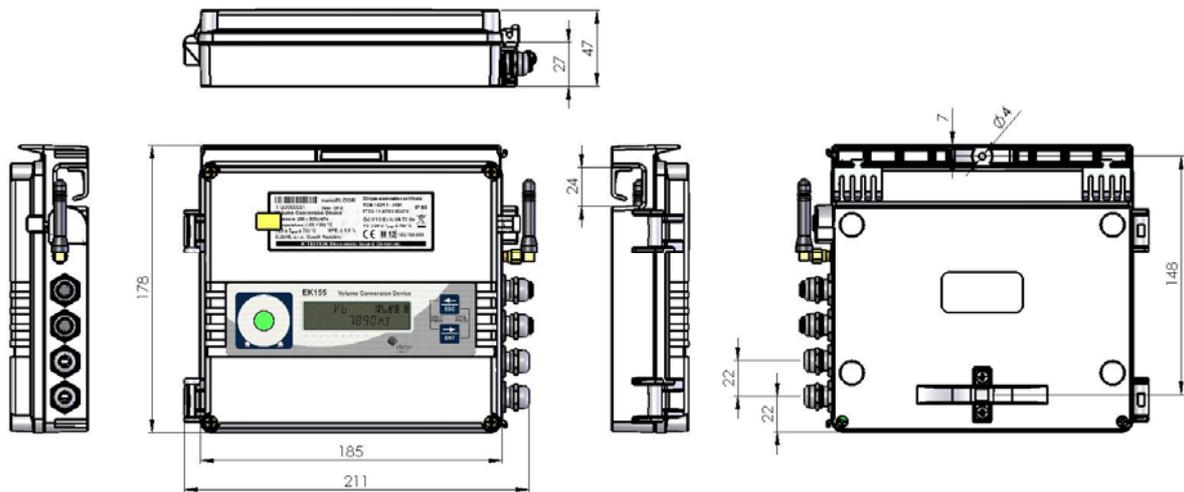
Dimensioni del dispositivo (senza copertura cavi)
